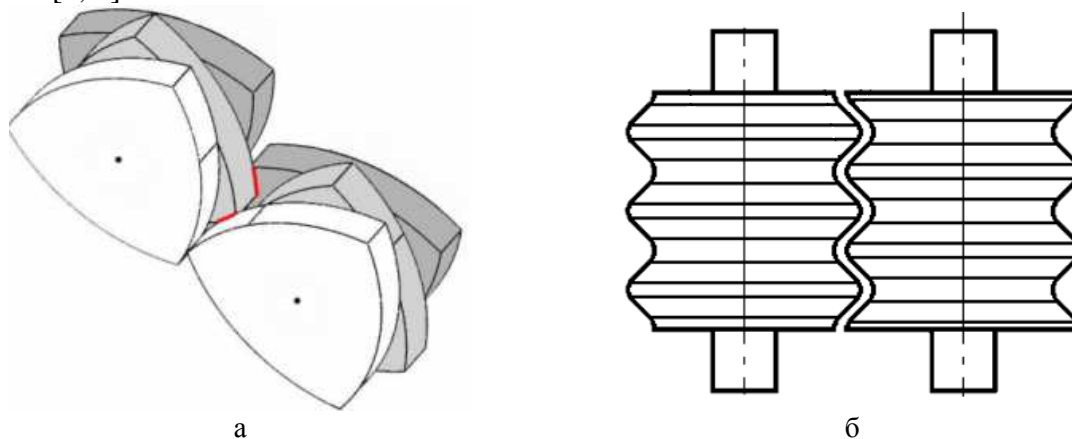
Модульная конструкция валков, состоящая из пластин в форме треугольника Рело (а) и валки с режущими элементами цилиндрической формы (б)
